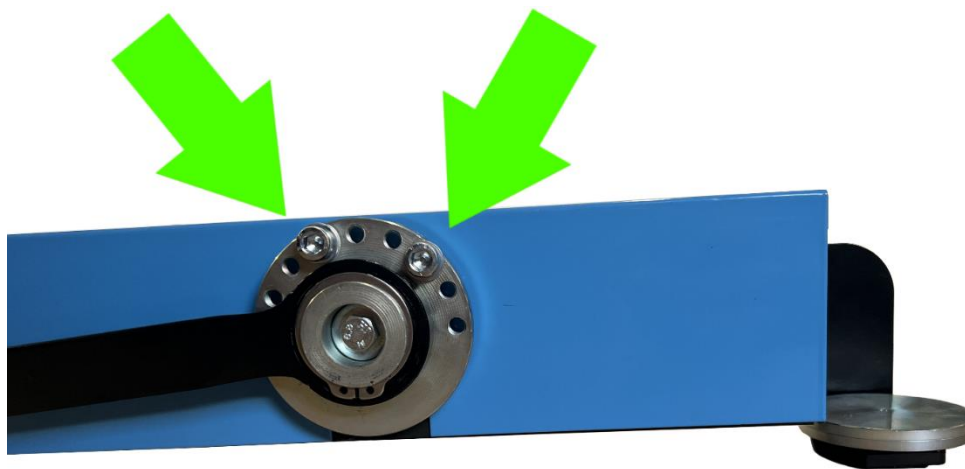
Viti a brugola da svitare per poter posizionare correttamente il braccetto
